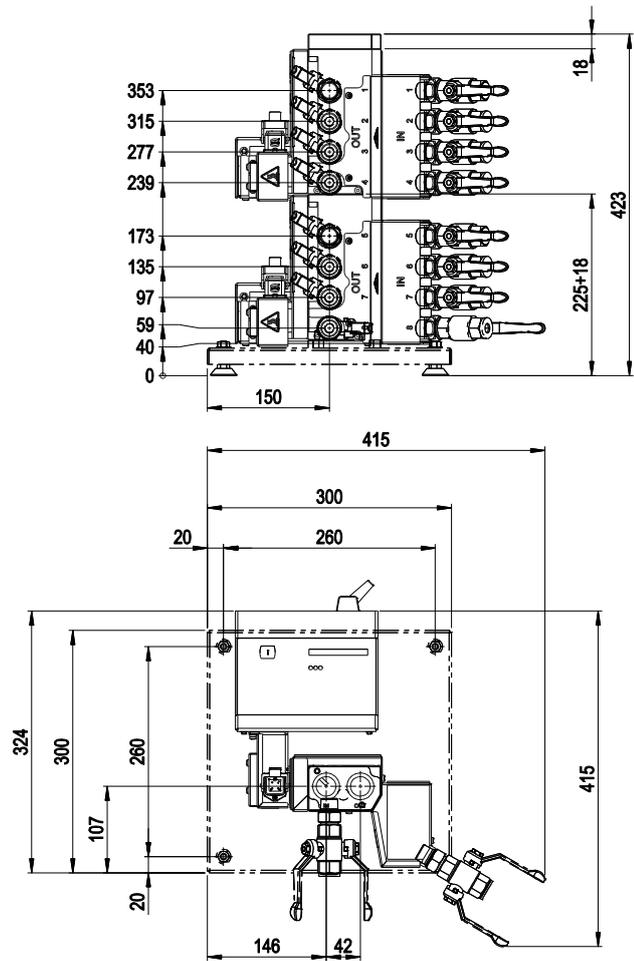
Размеры конструкции: отдельно стоящий прибор
